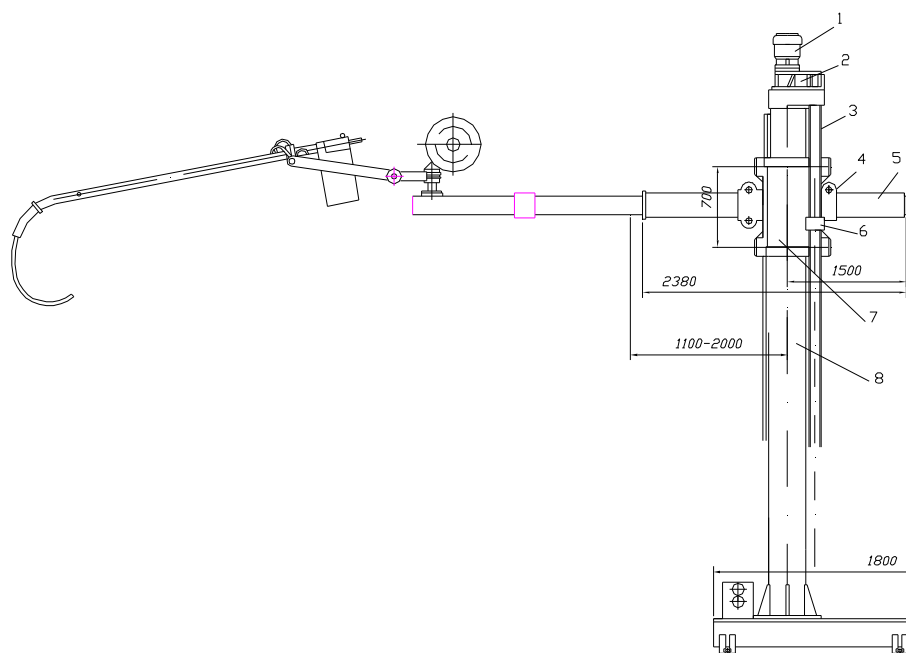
Сварочная консоль с полуавтоматом
